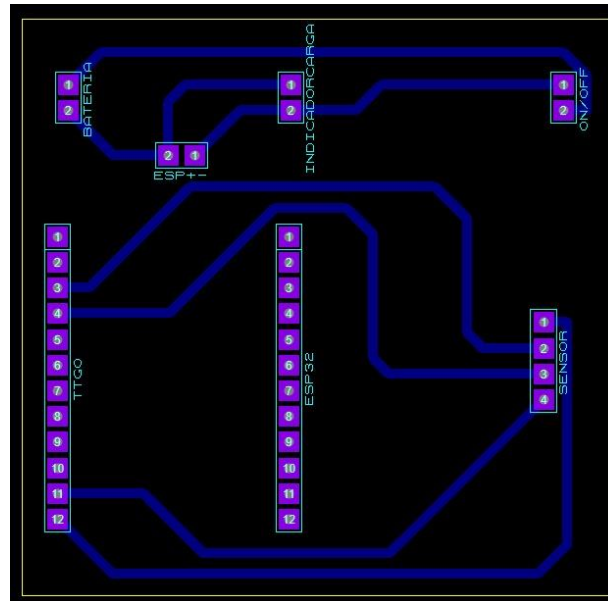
Vista de la placa PCB diseñada para el prototipo IoT
